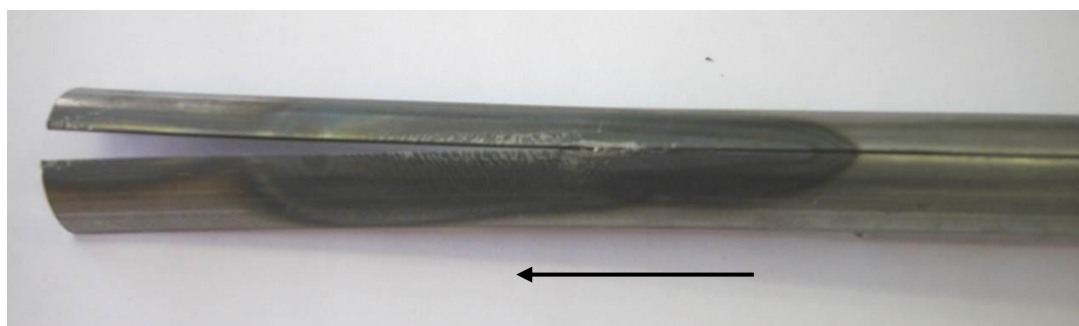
Нагрев и сварка трубной заготовки при оптимальном положении индуктора без образования выплеска. Диаметр трубной заготовки 25 мм.
